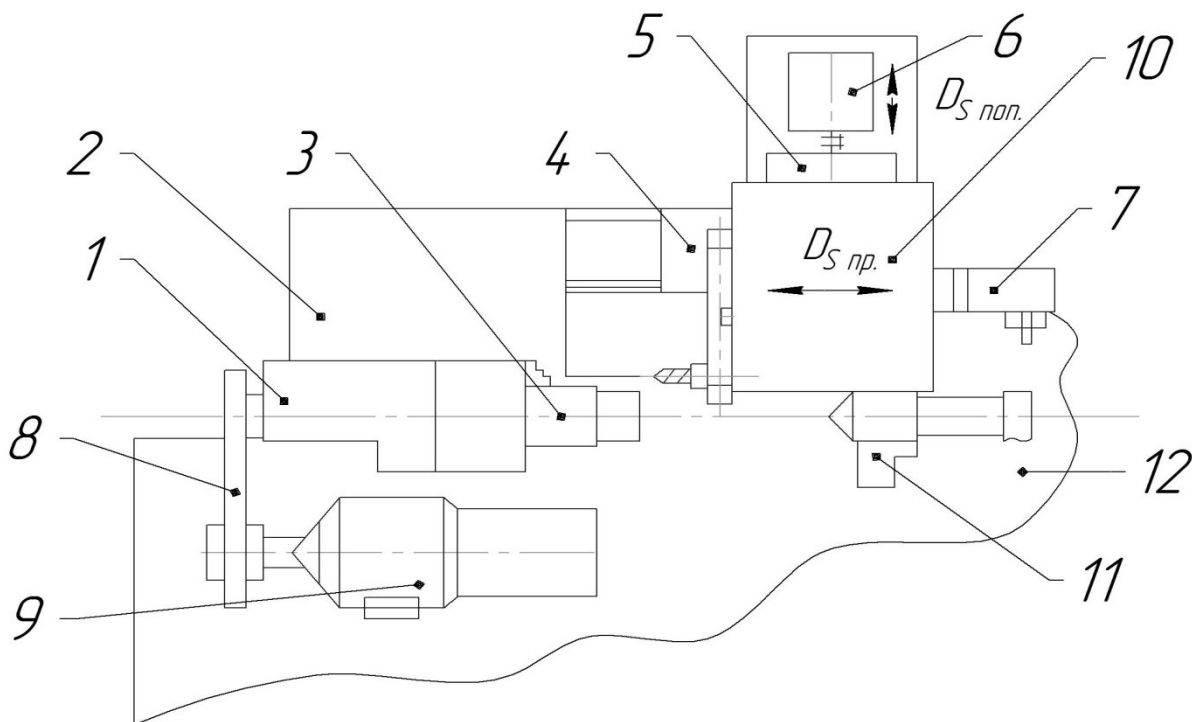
Основные узлы токарно-фрезерного станка EMCO CONCEPT TURN 155
